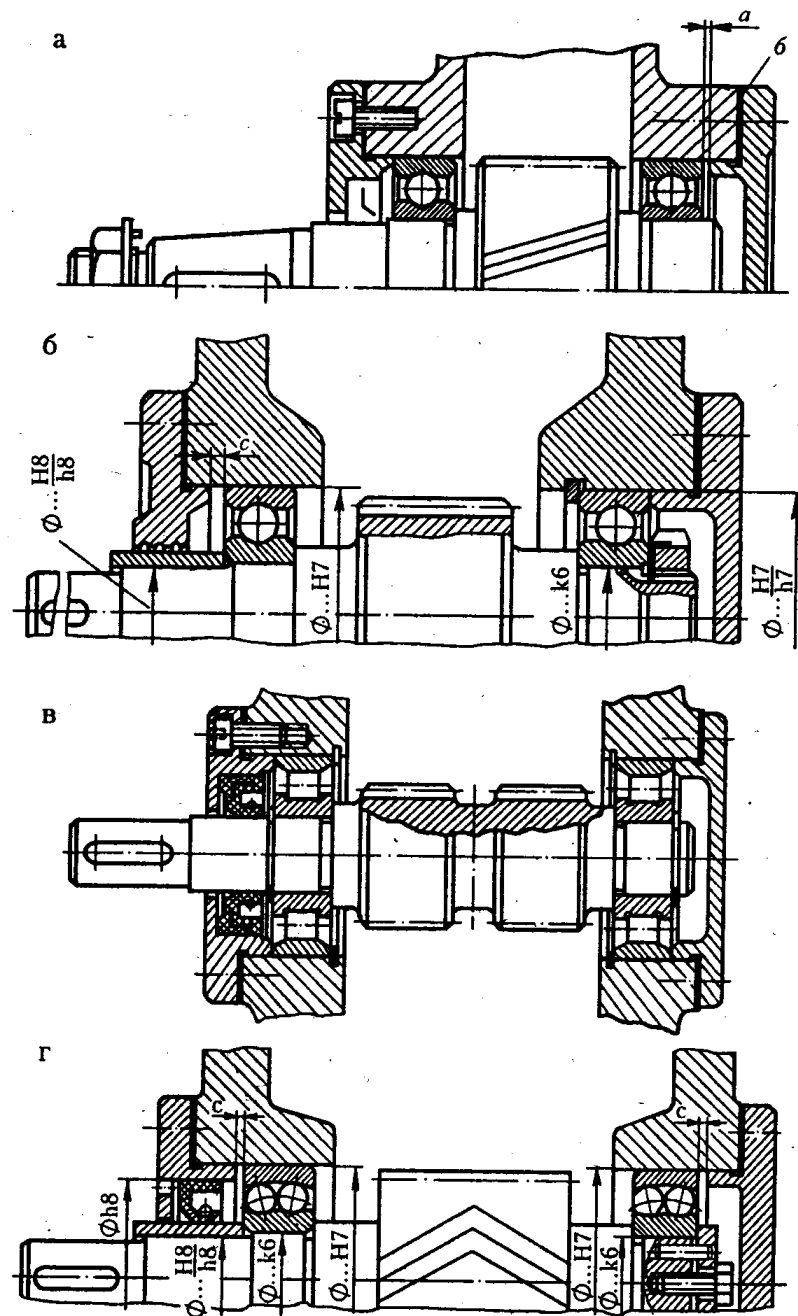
Конструктивні особливості опор валів з радіальними підшипниками
